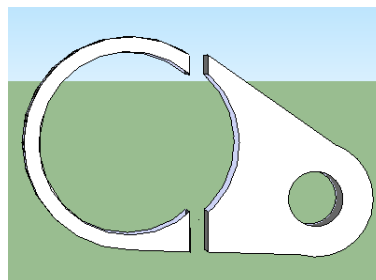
Accesorio utilizado para el anclaje del cable. (Detalles de proveedor, Manual "Terminales de vaciado abiertas Crosby")
